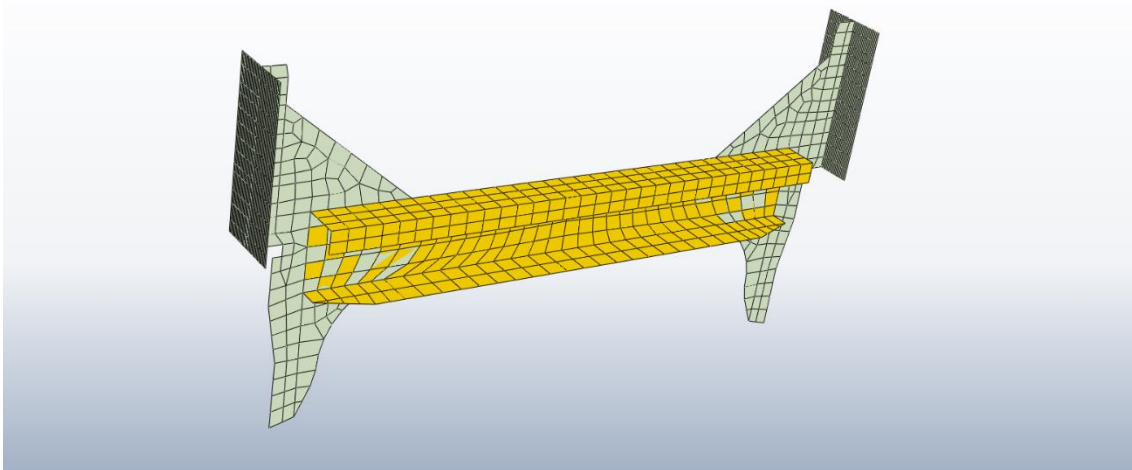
Malla del travesaño (amarillo) 427 nodos 384 elementos (x1 pieza) y de los refuerzos (gris) 724 nodos 656 elementos (x2 piezas)
